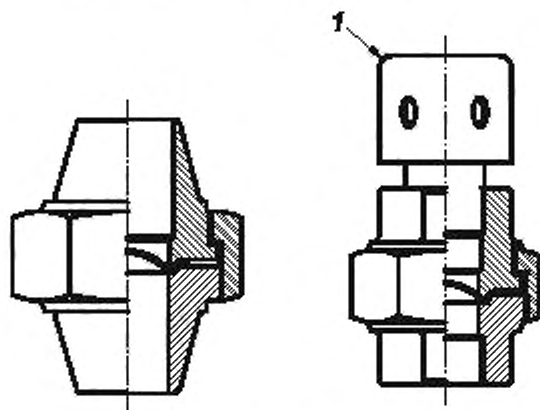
Типовой держатель разрывной мембраны с фланцем с полной уплотнительной поверхностью
